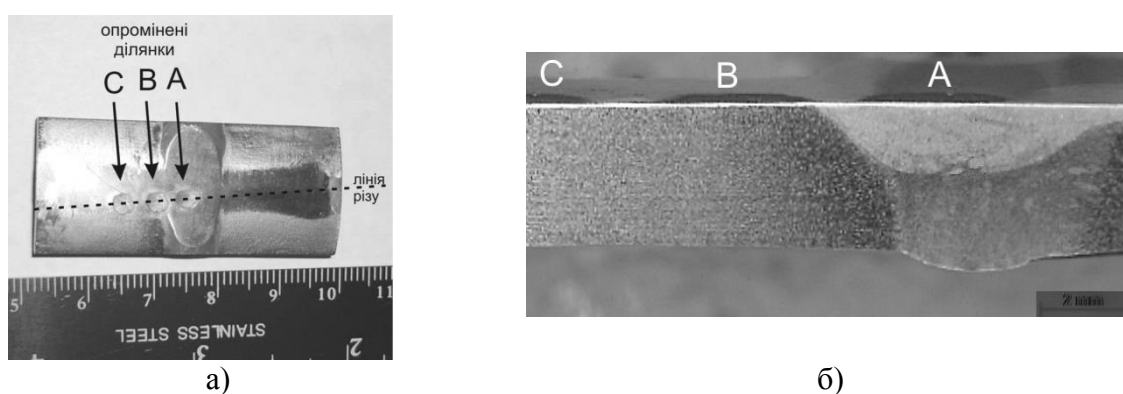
Схема вирізання та опромінення зразка зварного з'єднання: ділянка А над зварним швом, ділянка В та ділянка С над зоною термічного впливу зварювання
